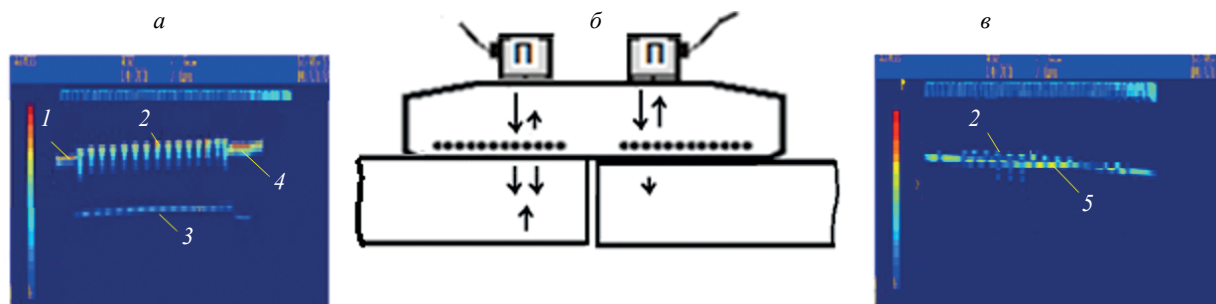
Изображение В-сканов сечения сварного муфтового соединения полиэтиленовых труб согласно [12]:
